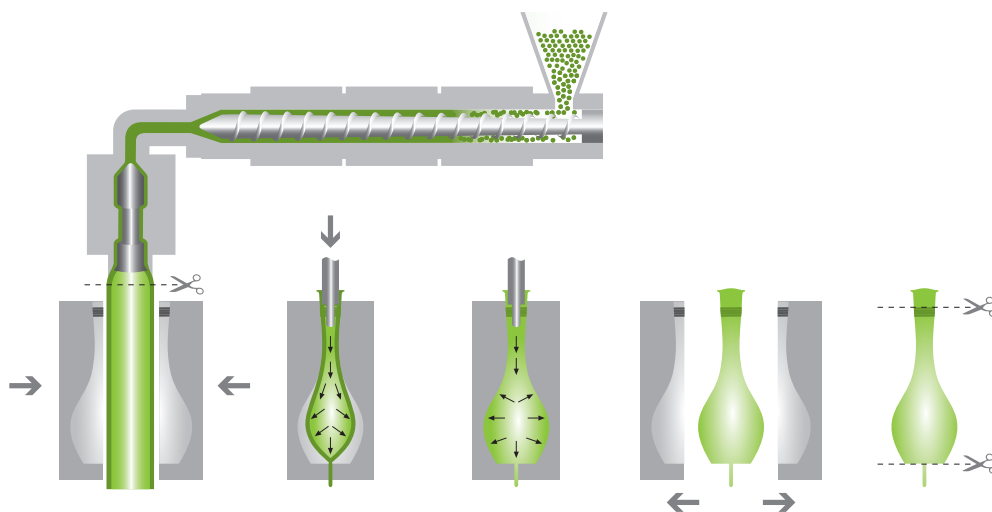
Esquema del proceso de extrusión soplado de cuerpo hueco.
